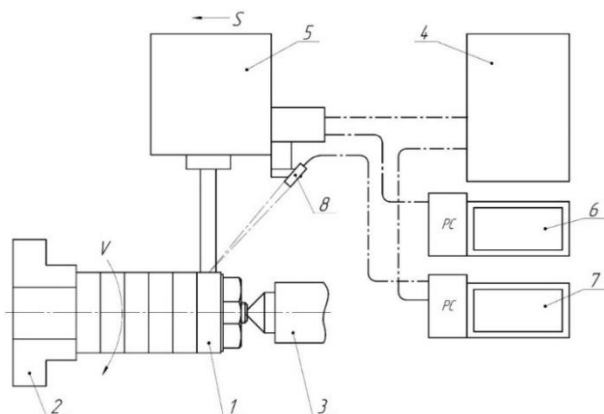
Схема лазерной закалки: 1 – заготовка; 2 – патрон; 3 – задний центр; 4 – источник лазерного излучения; 5 – оптическая головка; 6 – контроллер ЧПУ; 7 – контроллер температуры; 8 – пирометр
